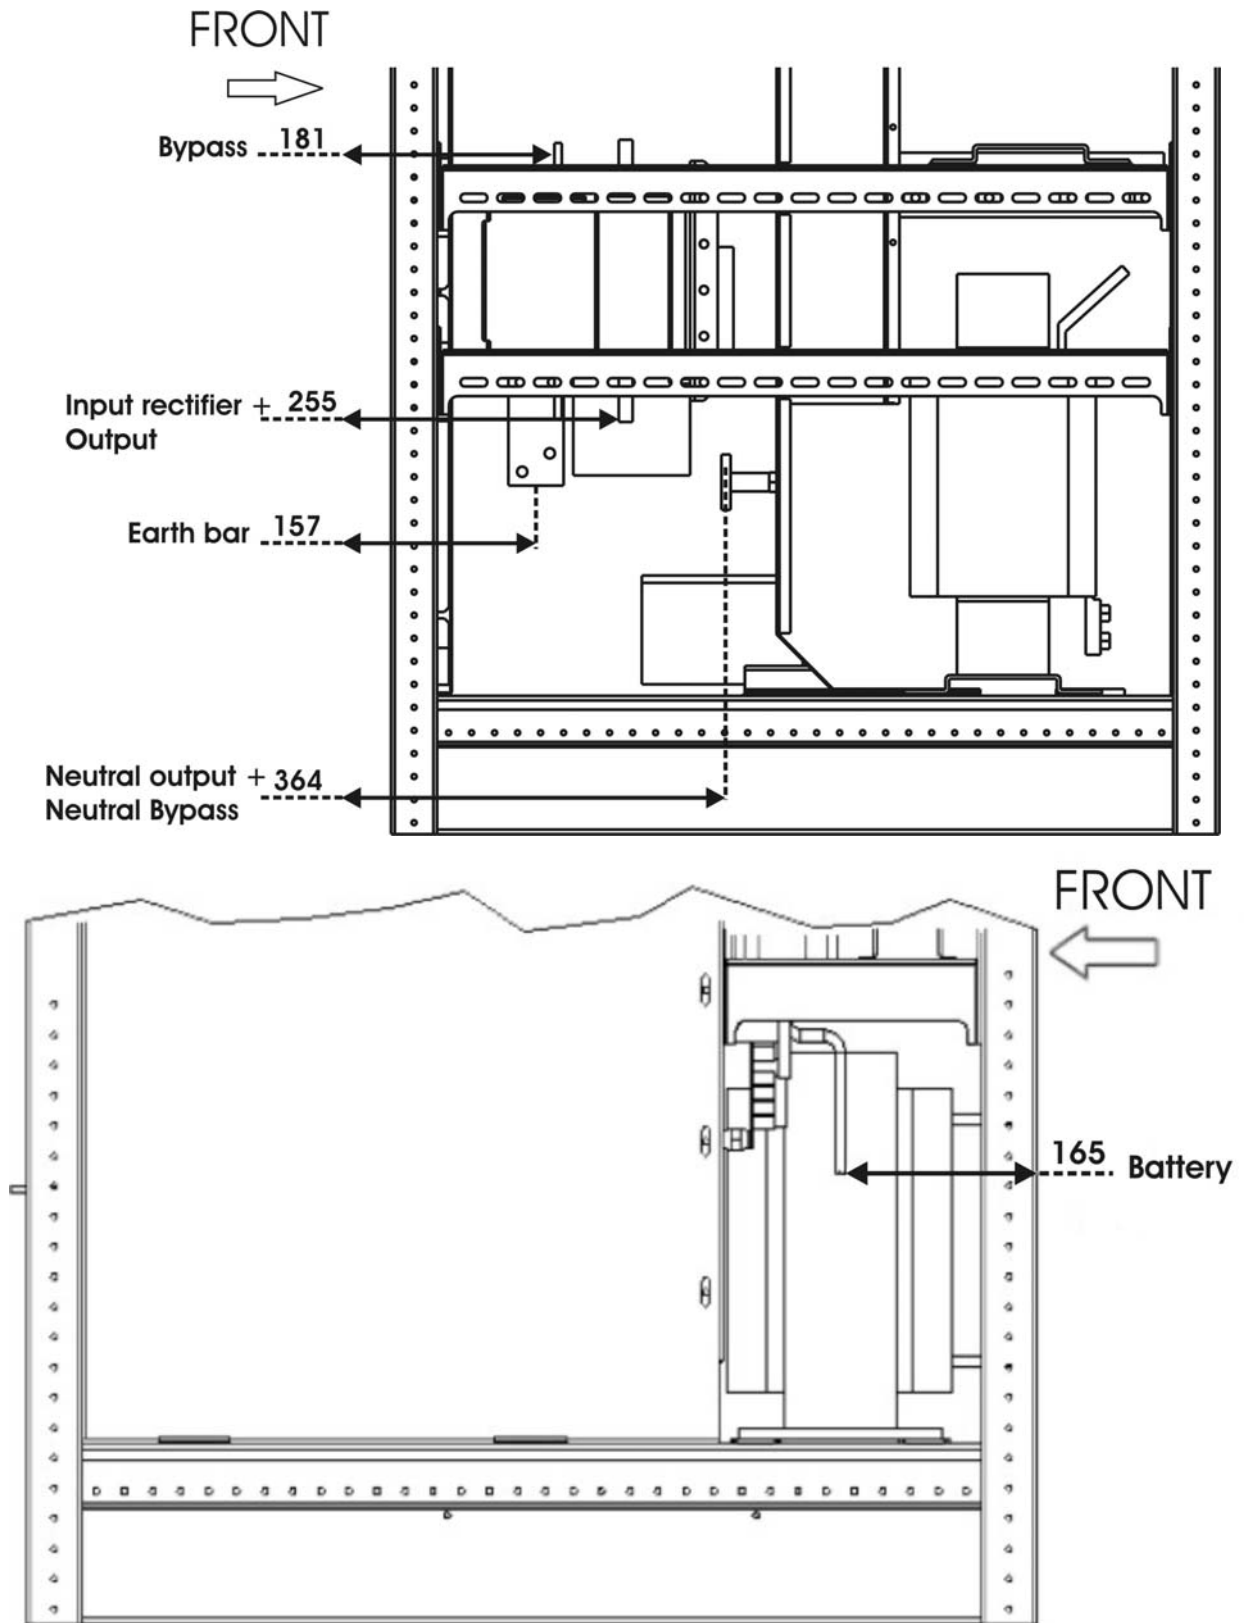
Vue latérale du bornier du KEOR HP 500-600-800 kVA
